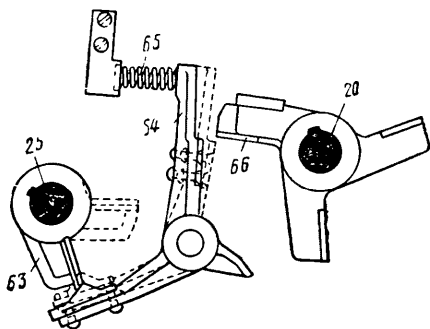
Механическая блокировка между главным и тормозным валами контроллера (запор главной рукоятки при рабочих позициях торможения): 20—вал главного барабана; 25—вал тормозного барабана; 63—рычаг; 64—рычаг; 65—пружина; 66—звездочка
